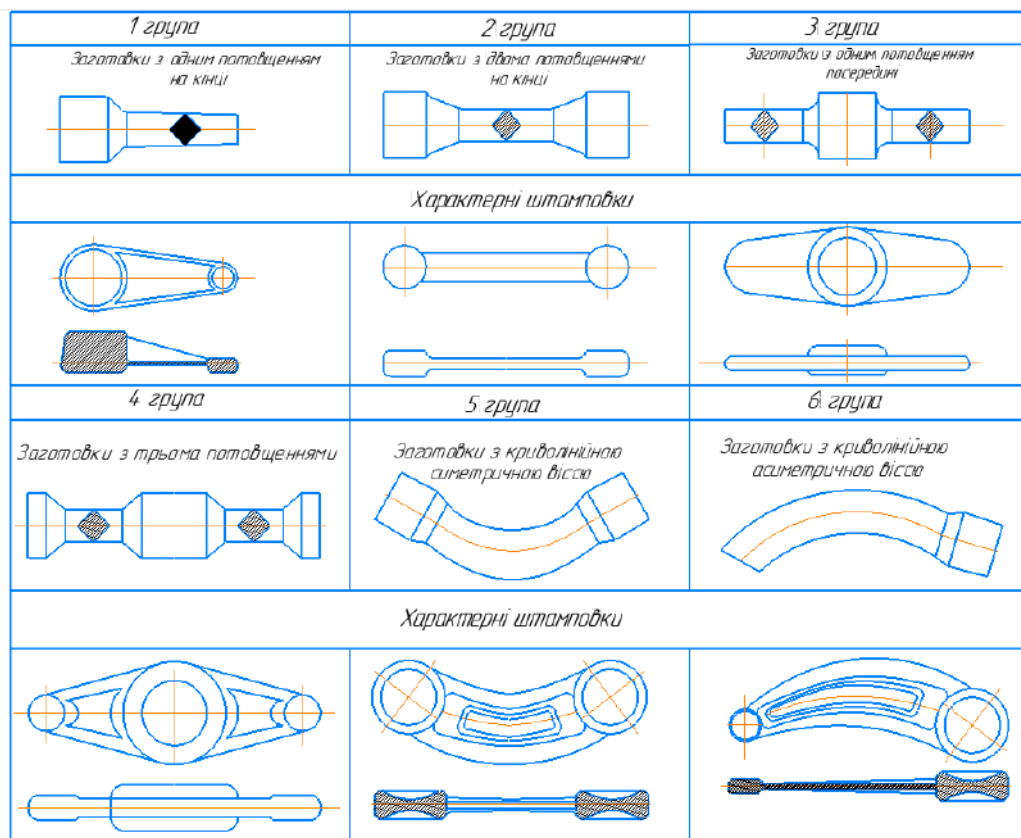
Типові представники заготовок складного поперечного перерізу
